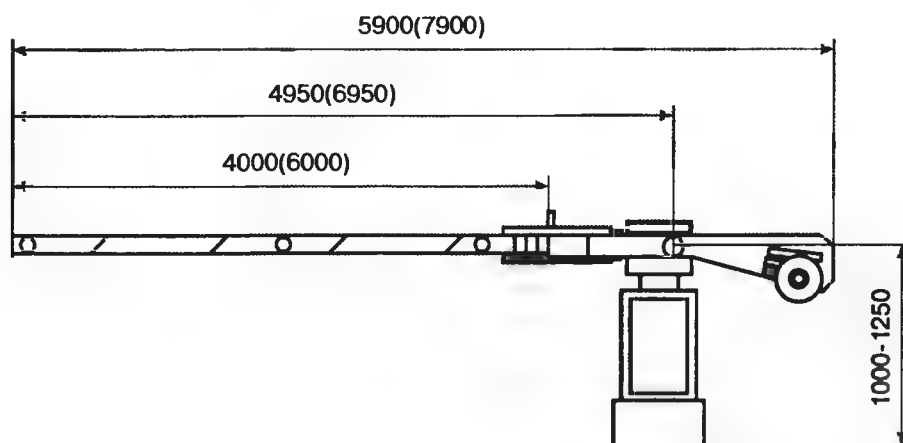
Шлагбаум автоматический типа ПАШ1 (размеры без скобок для ПАШ1-5, размеры в скобках для ПАШ1-6)
